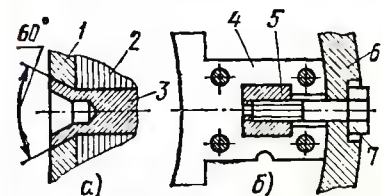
Крепление листов сердечника полюса заклепками (а) и стержнем (б)
